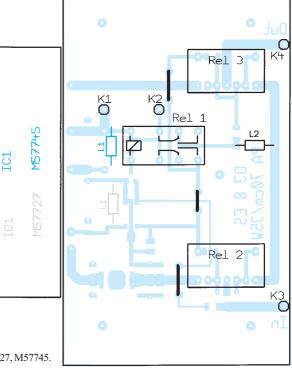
Bestückung der wenigen Bauelemente auf der Platinenoberseite; graue Bezeichnungen betreffen die 2-m-Variante, blaue 70 cm.
